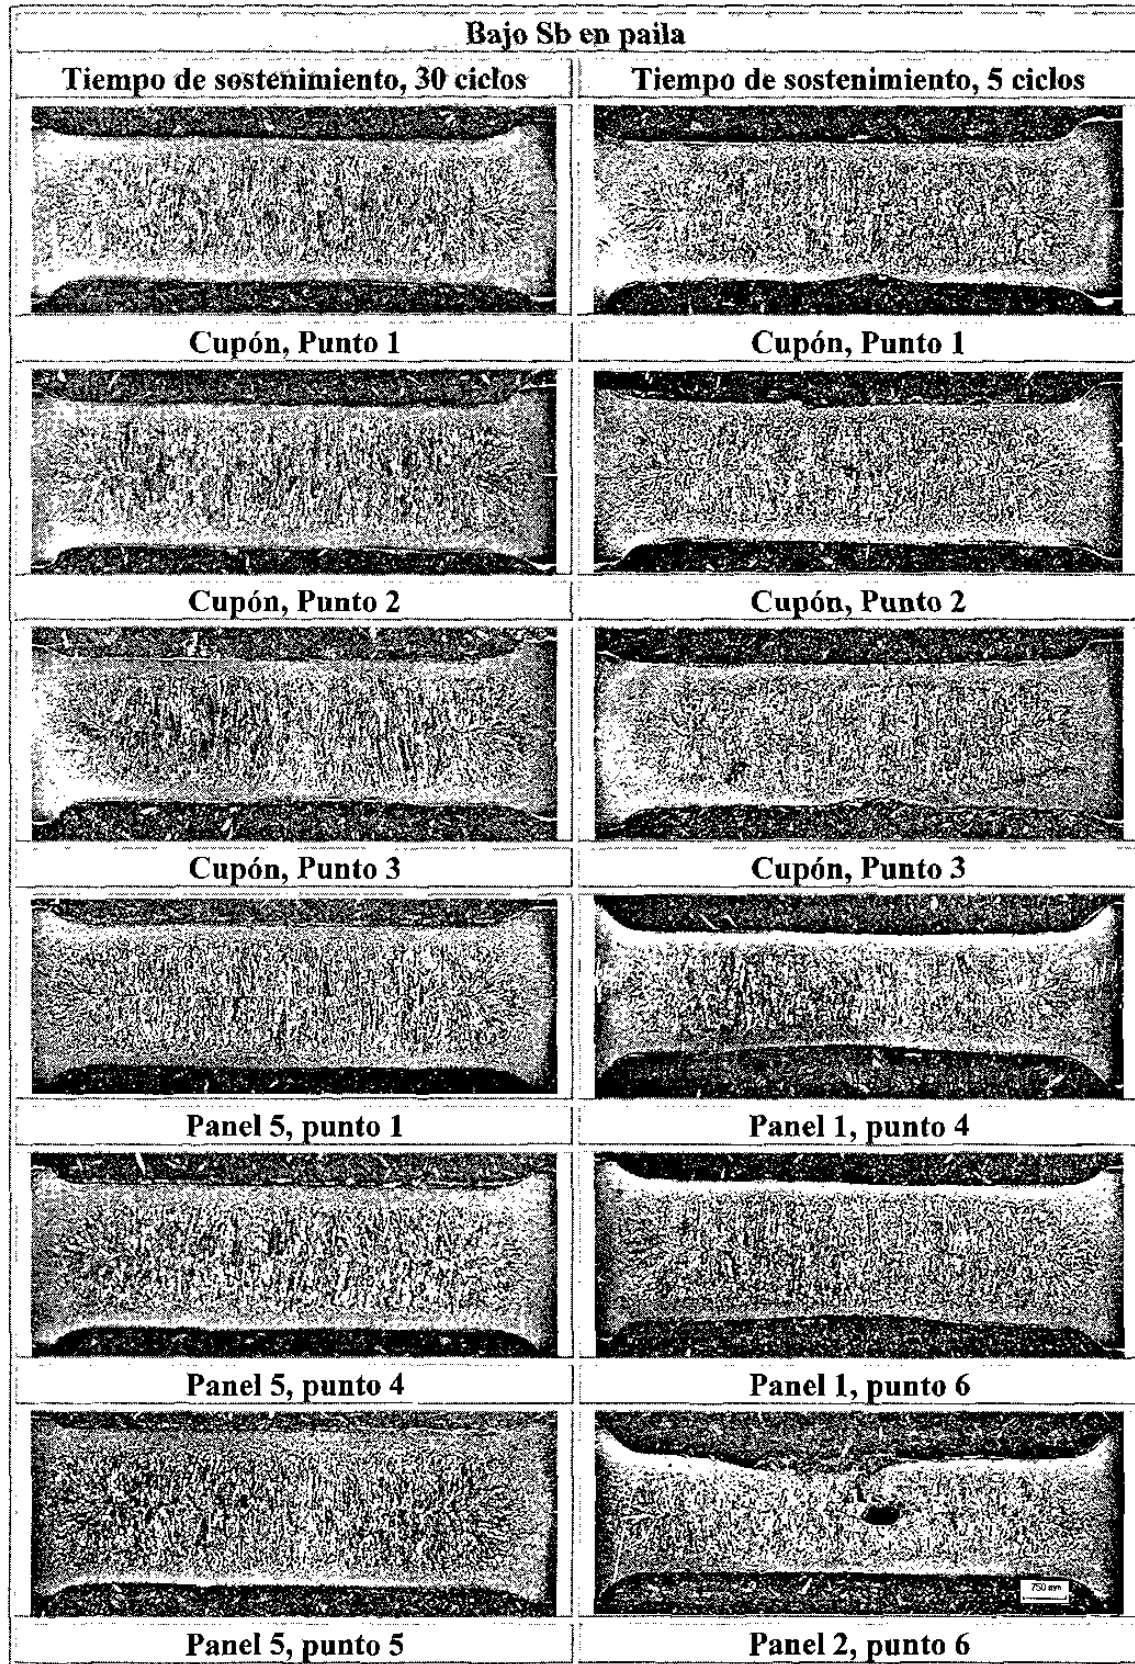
Sección transversal del botón de soldadura para la prueba de bajo Sb.
